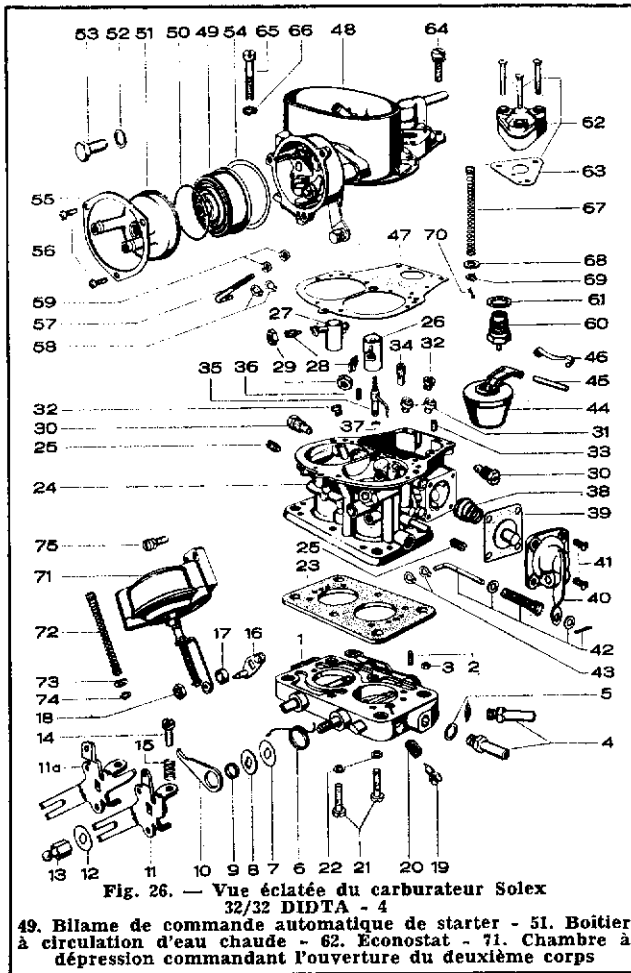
Vue éclatée du carburateur Solex 32/32 DIDTA - 4
